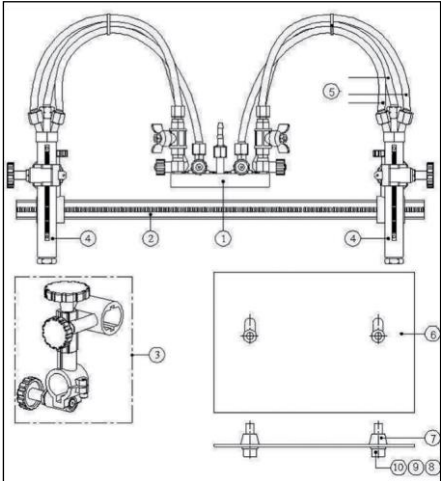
Conjunto de expansão com o segundo maçarico de corte
